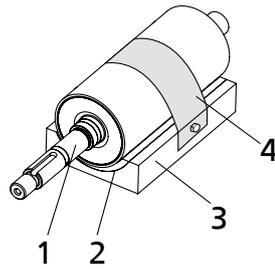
Hilfsvorrichtung Montage/ Demontage motorseitige Lagerhülse
